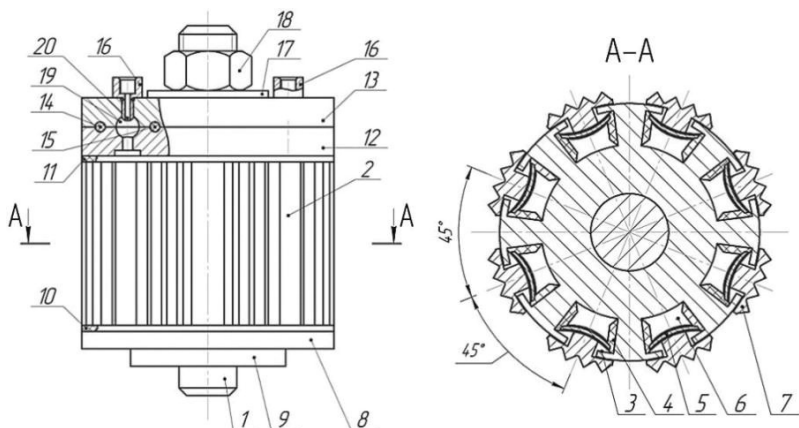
Зовнішній вид гідропластичної оправки з корончатим видавлювачем.
